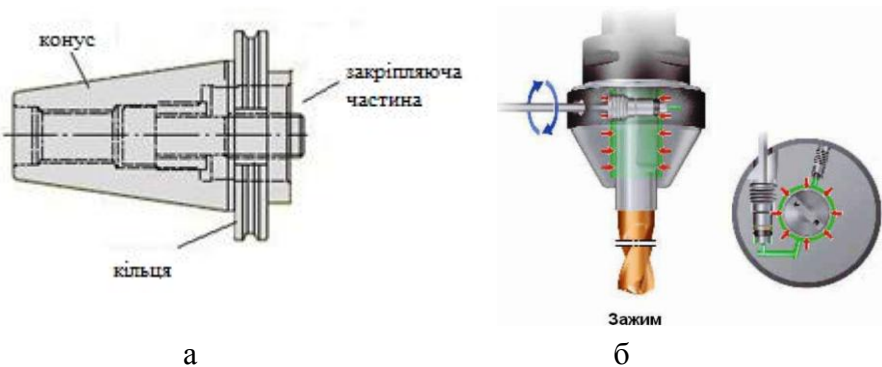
Фрезерна оправка (а) та оправка з гідропластом (б)
